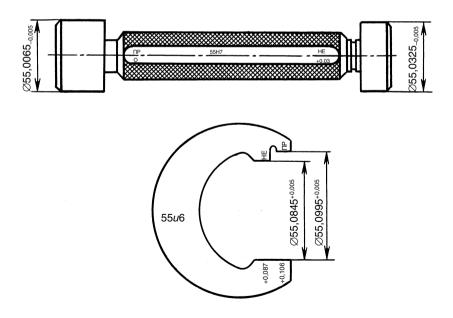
Калибры для контроля деталей ⊘55H7 и ⊘55u6
